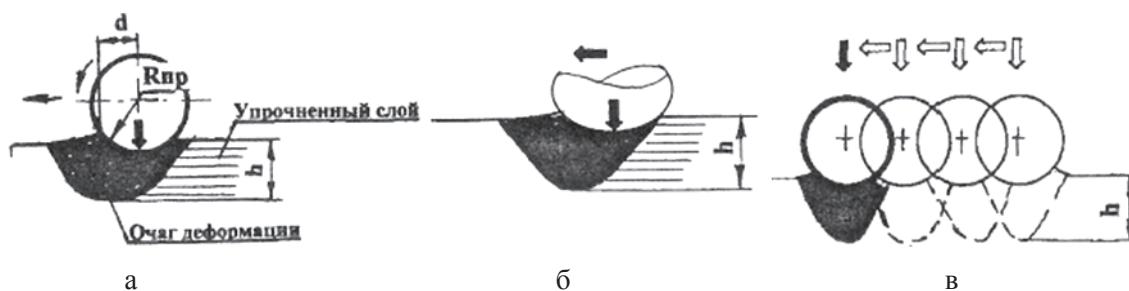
Основные схемы взаимодействия деформирующего элемента с обрабатываемой поверхностью: а – качение; б – скольжение; в – внедрение
